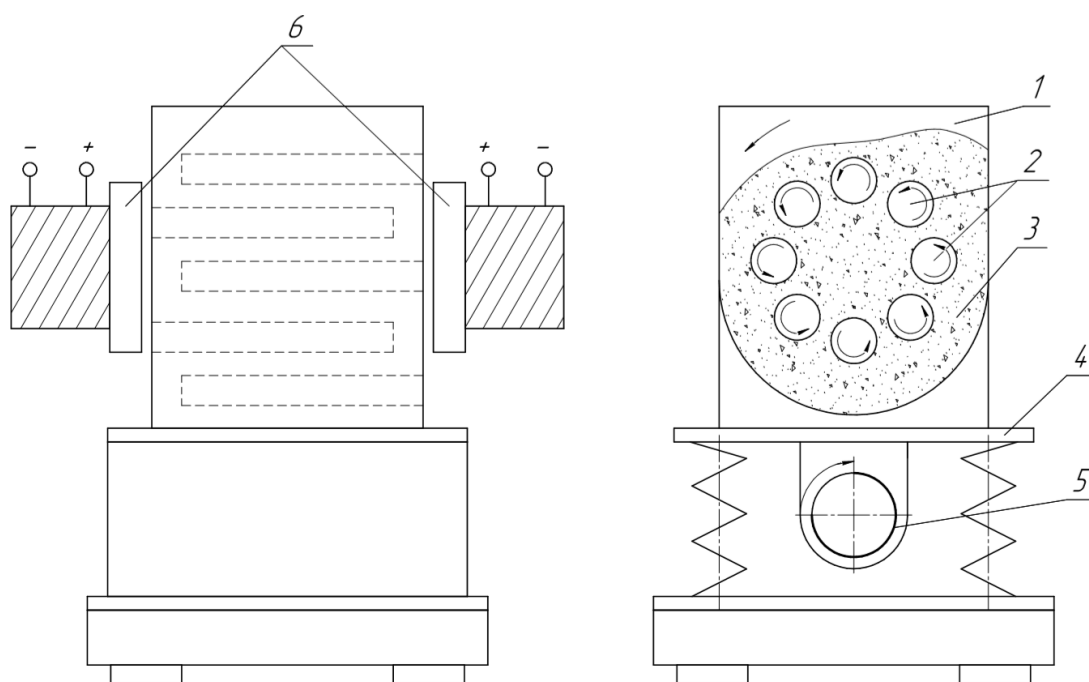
Схема устройства для магнитно-вибраоабразивной обработки:
